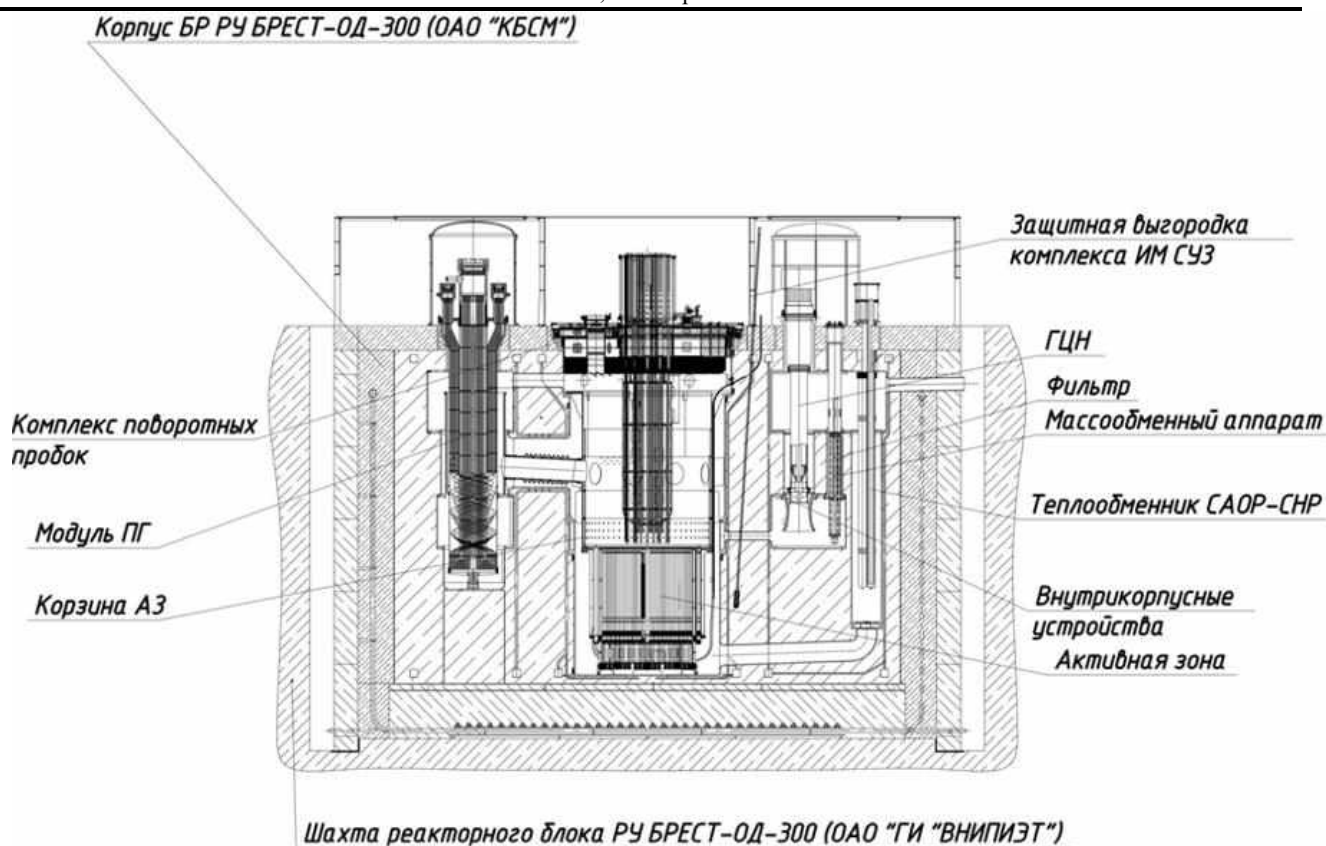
Корпус БР РУ с оборудованием
